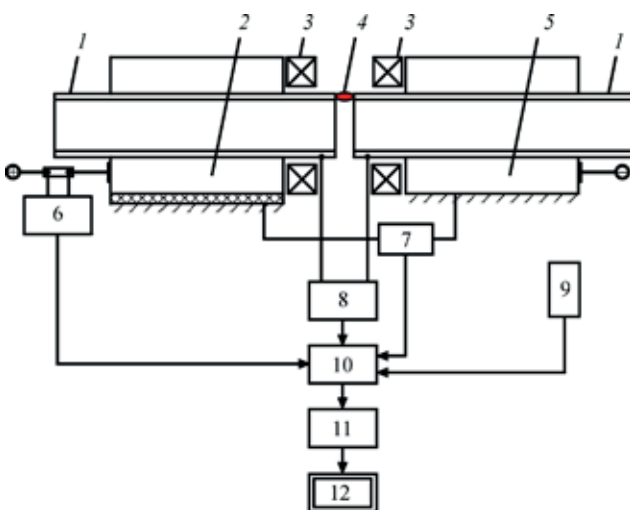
Блок-схема макету контролю якості зварюваних з'єднань: 1 – зварювані труби; 2 – рухомий затискний пристрій; 3 – елементи магнітної системи; 4 – стовп електричної дуги, яка рухається по кромках зварюваних труб; 5 – нерухомий затискний пристрій; 6 – датчик струму з інструментальним підсилювачем сигналу; 7 – датчик положення рухомої частини зварювальної установки; 8 – датчик падіння напруги на зварювальній дузі; 9 – датчик вимірювання абсолютного тиску гідравлічної системи, вбудований в штокову порожнину циліндру осадка зварювальної машини; 10 – нормуючий інструментальний підсилювач (з ФНЧ $F_{сп} = 100$ Гц); 11 – приймаючий аналогово-цифровий перетворювач (АЦП); 12 – персональна електронно-обчислювальна машина
